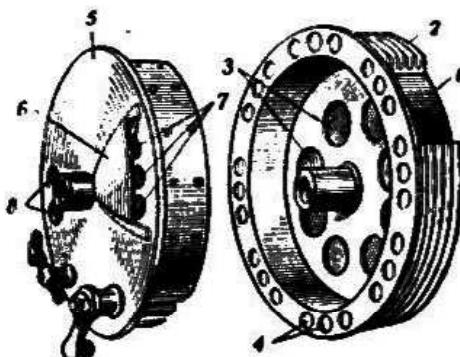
Тормозной барабан мотоцикла М-35 со стальными ребрами:
